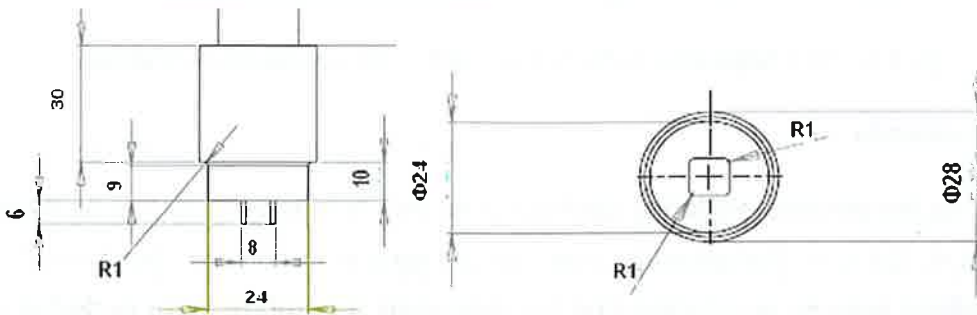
Herramienta A para FSW CIDESI. Dimensiones en mm.
